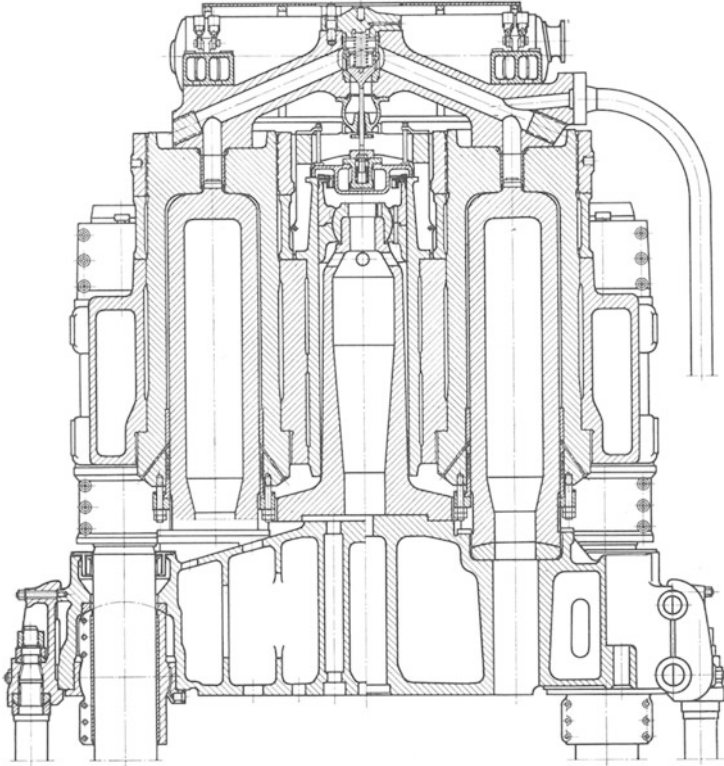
Querhaupt für eine 10000-t-Zweizylinder-Schmiedepresse mit kombinierter Säulen- und Stempelführung, sowie kugelliger Lagerung der Gleitschuhe. (Kreuser G. m. b. H., Hamm i. W.)
